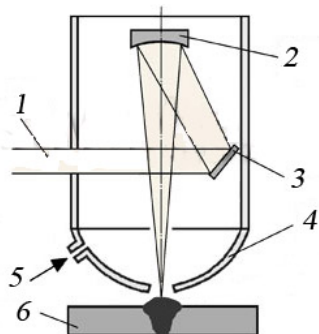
Схема лазерного зварювання: 1 – промінь лазера; 2 – фокусуювальне дзеркало; 3 – відбивальне дзеркало; 4 – корпус; 5 – захисний газ; 6 – виріб – стрічкова пилка
